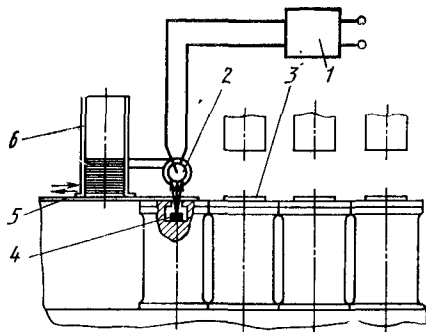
Бесконтактный радиоизотопный КБУ для контроля толщины заготовки
